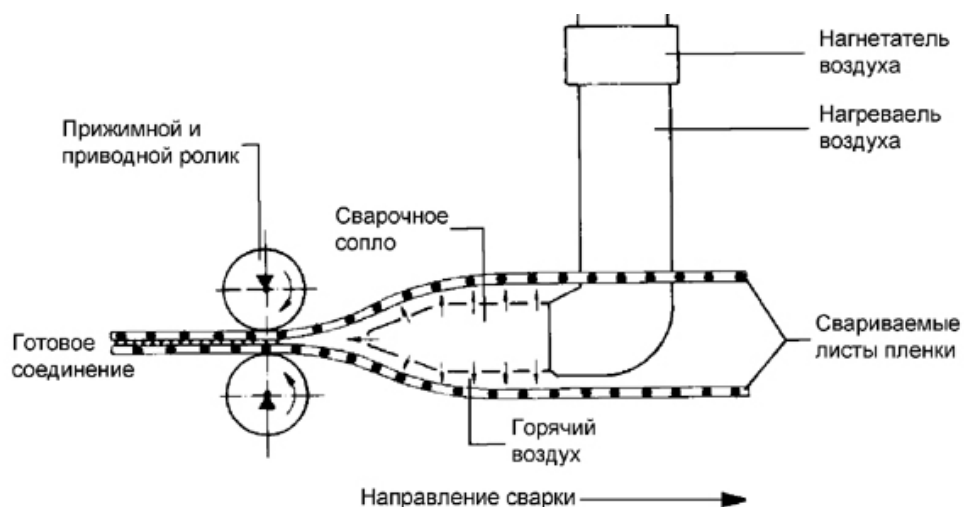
Автоматические машины для сварки пленки горячим воздухом
